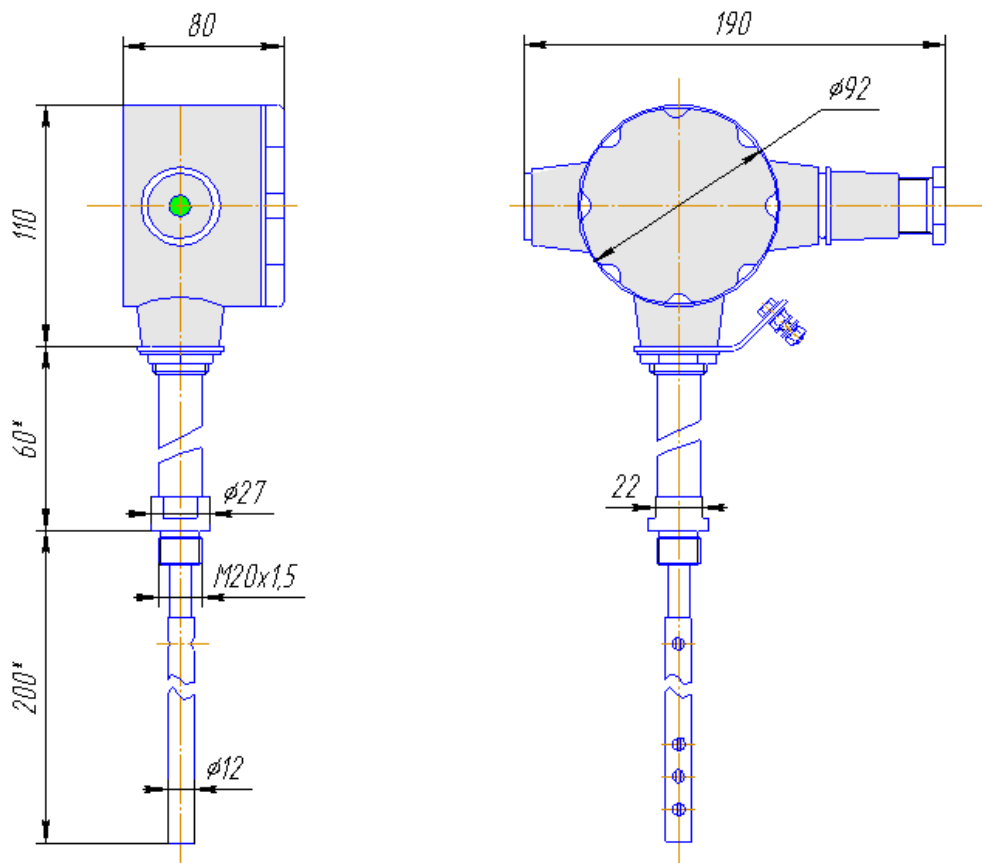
Внешний вид и габаритные размеры прибора СЖУ-1-АИ.
